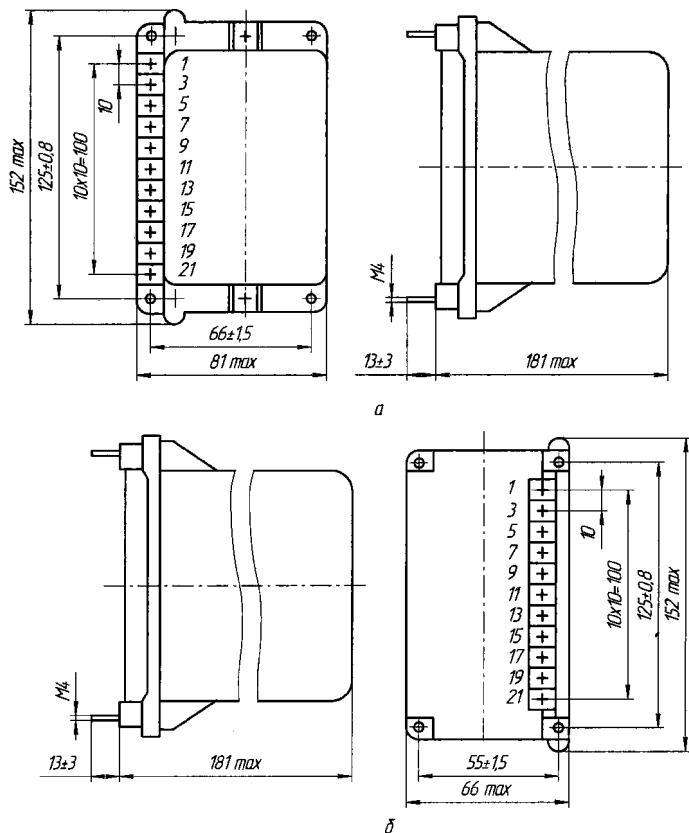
Габаритные, установочные и присоединительные размеры реле типа РПВ 01.
